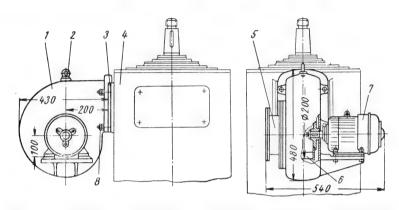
Установка вентилятора на двигателе поворотного механизма
